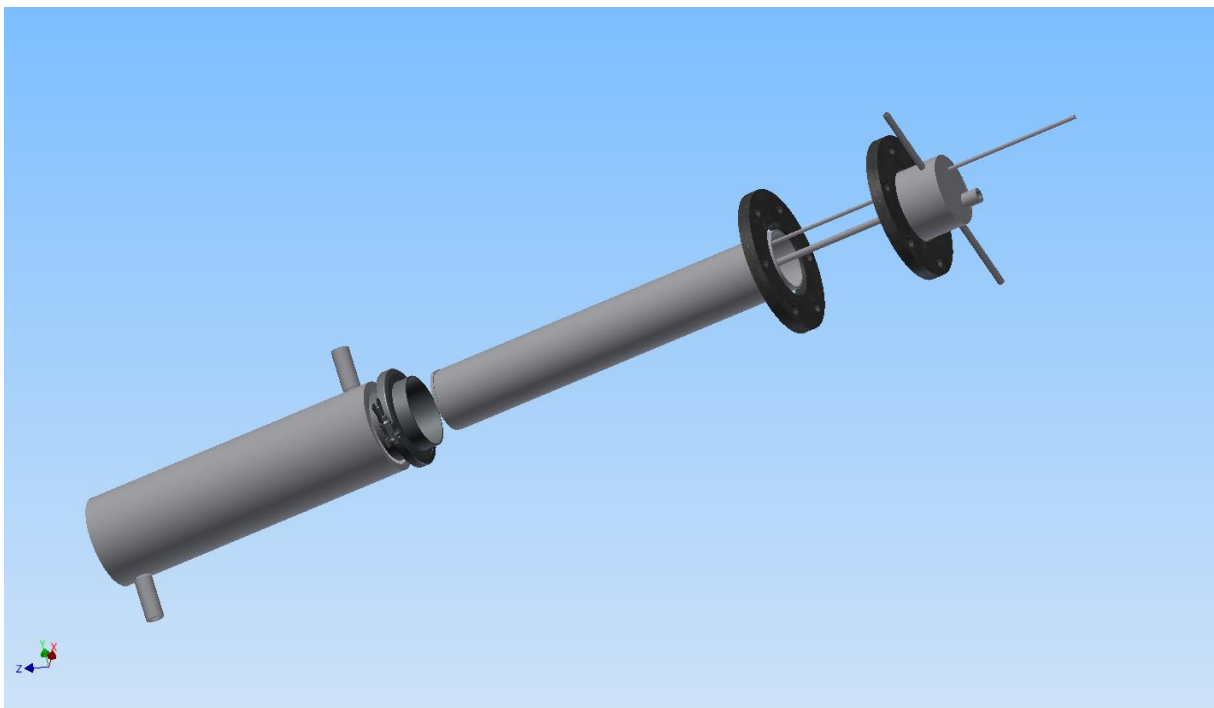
CAD Zeichnung der Kühlfalle
